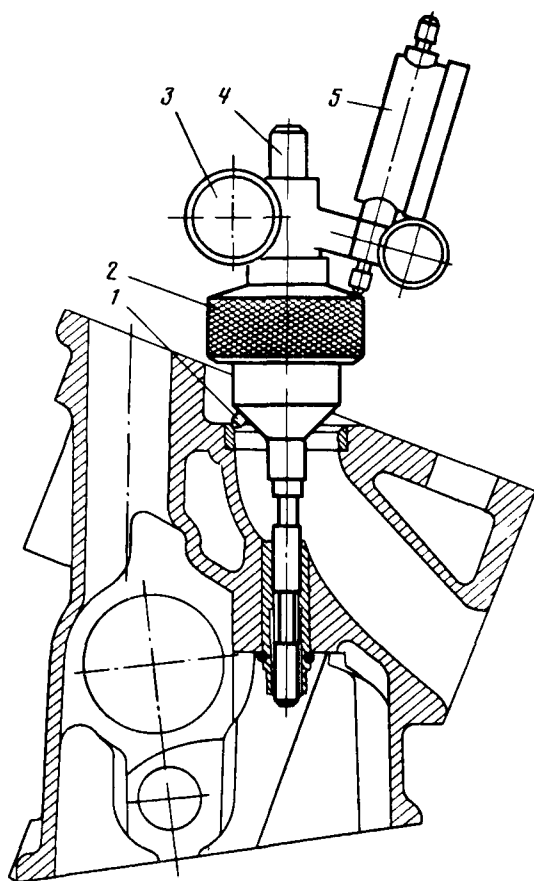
Приспособление для проверки concentричности фаски седла клапана оси направляющей втулки:
